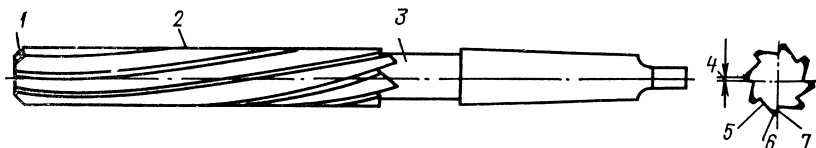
Элементы конструкции разверток: 1, 2 — режущая и калибрующая части; 3 — корпус (хвостовик); 4 — ленточка; 5 — стружечная канавка; 6 — задняя поверхность зуба; 7 — передняя поверхность зуба
